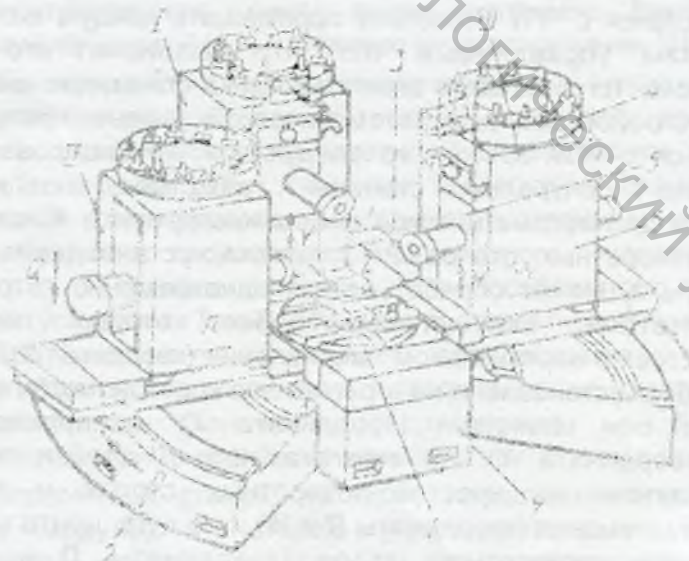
Компоновка переналаживаемого агрегатного станка с ЧПУ
